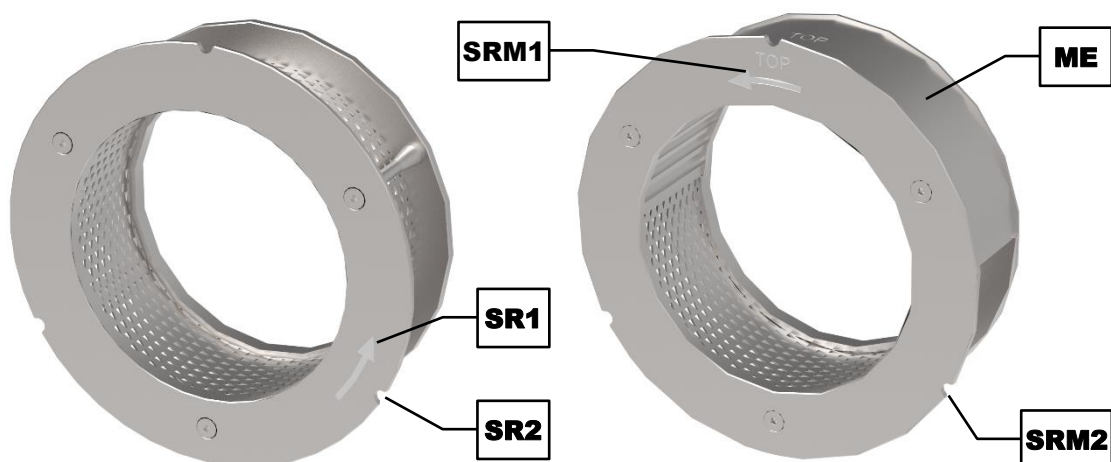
Siebrahmen für 360° Siebeinsätze (links) und 180° Siebeinsätze (rechts)
